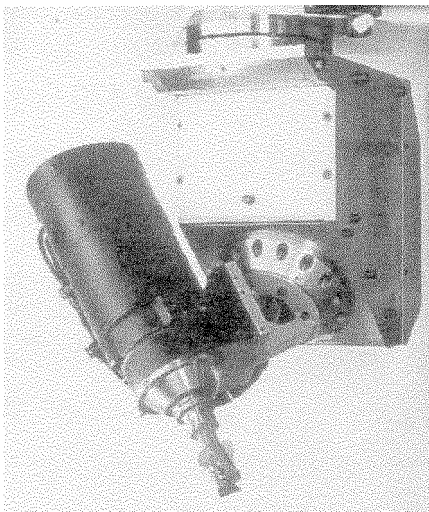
Werkzeugträger mit schiefwinkligen Achsen
